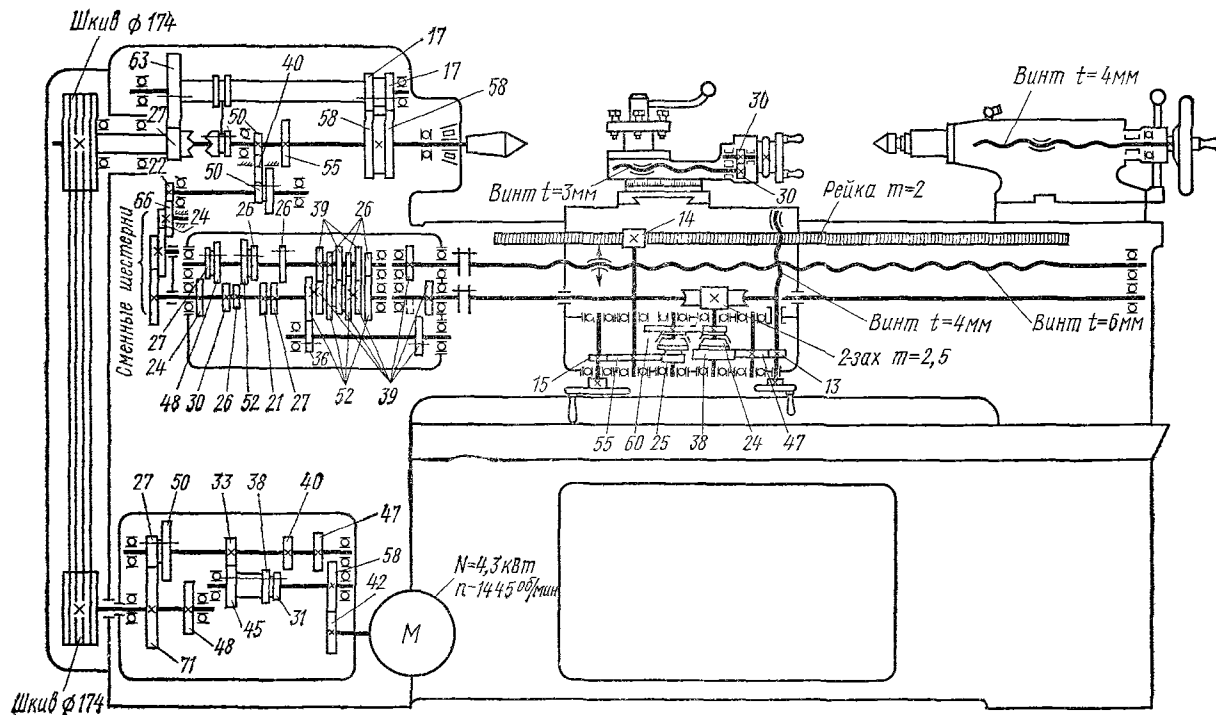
Кинематическая схема станка 1616 (цифрами обозначены числа зубьев)
